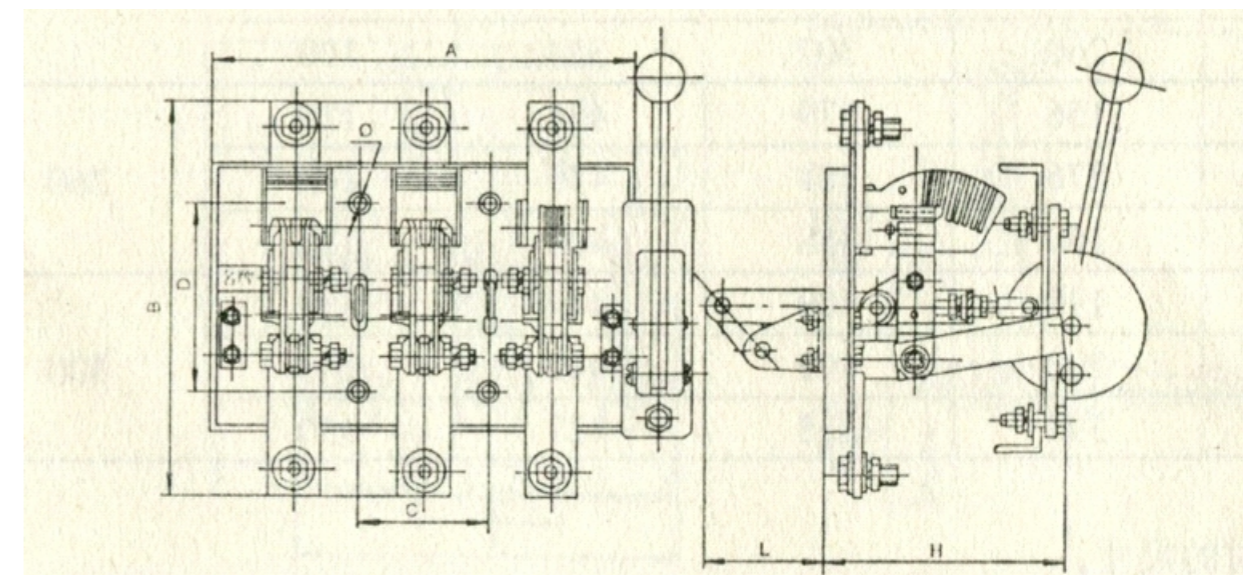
侧方正面杠杆操作机构式 (630-1600A) (尺寸见表5)
